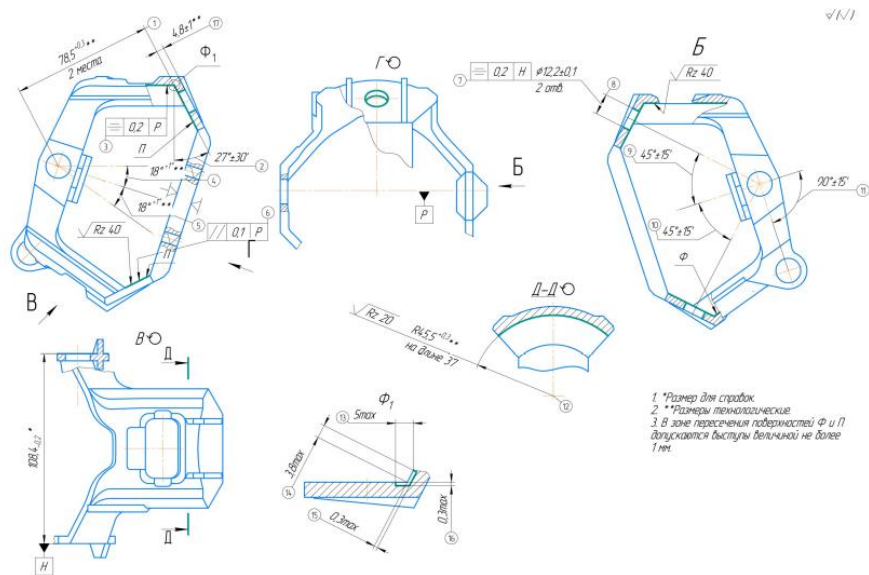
Эскиз к операции 055 – Фрезерная с ЧПУ
